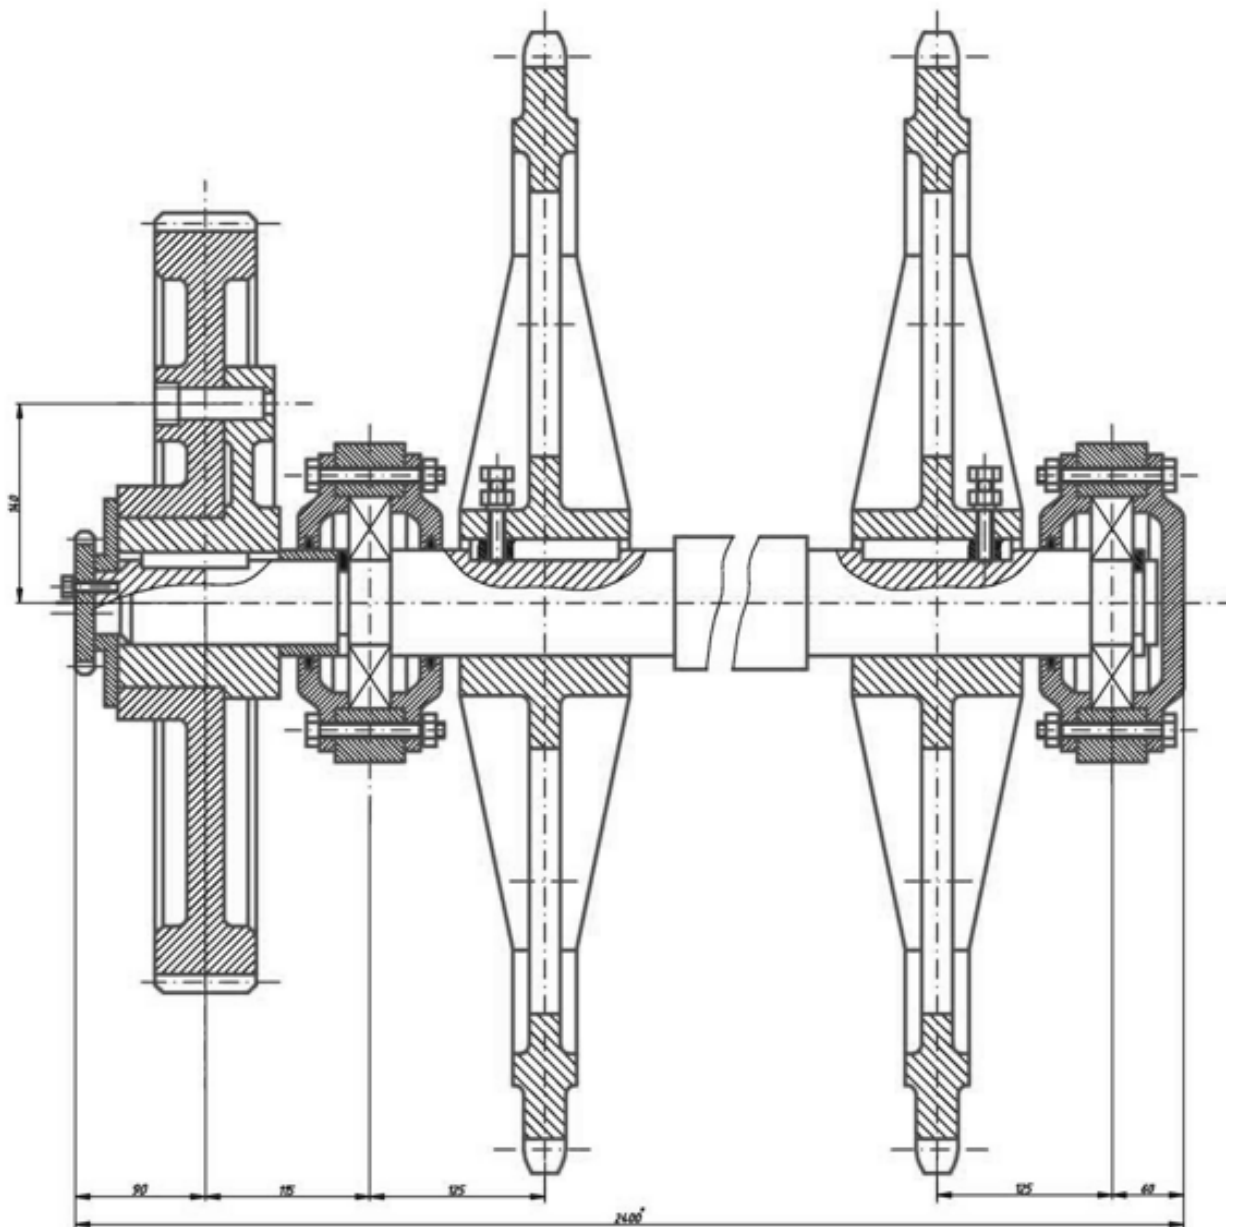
Вузол вала привідного приводу розстійної шафи агрегату
